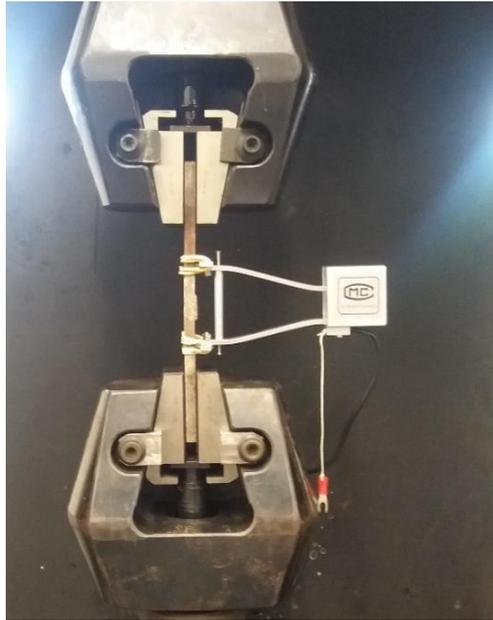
Representação de corpos de prova feitos por Procedimento de Soldagem. Fonte: UFTM, 2021.
